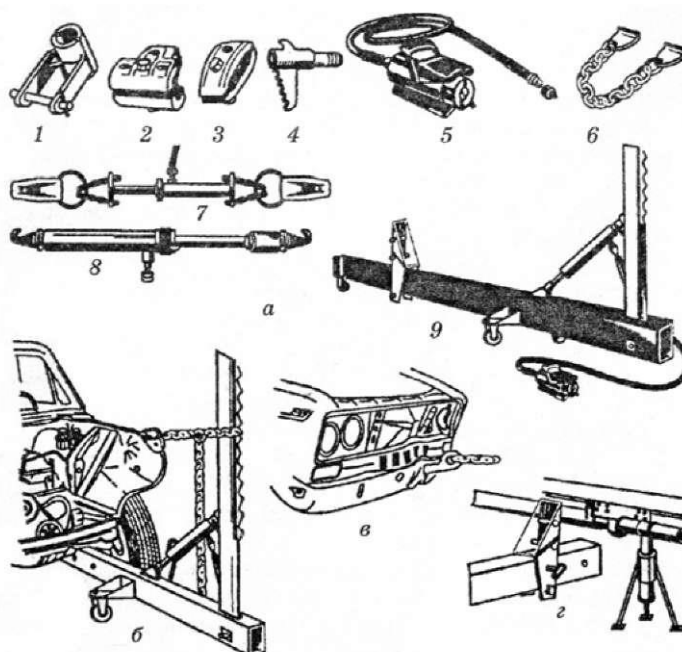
Приспособления для выполнения правки деформированного участка кузова: а-комплект приспособления для устранения перекосов и перегибов; б, в и г - использование приспособлений при правке; 1 - оправка для вытягивания вогнутых деталей; 2 и 3 -самозакрепляющиеся
